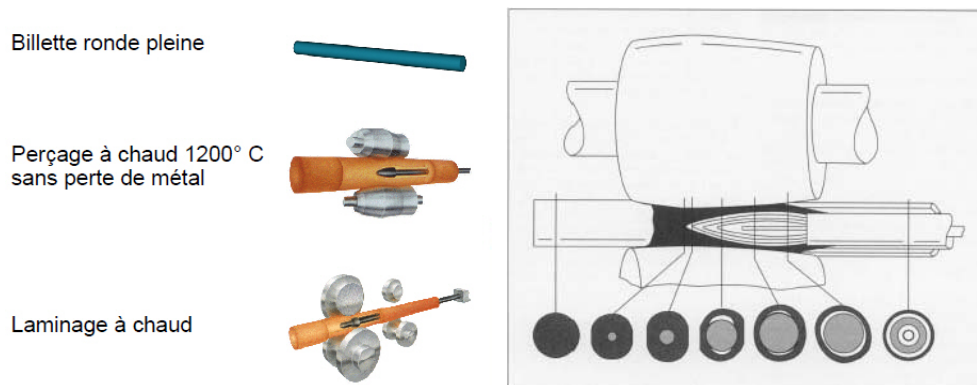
Mise en forme de l'acier par laminage de tube sans soudure (d'après Vallourec).
